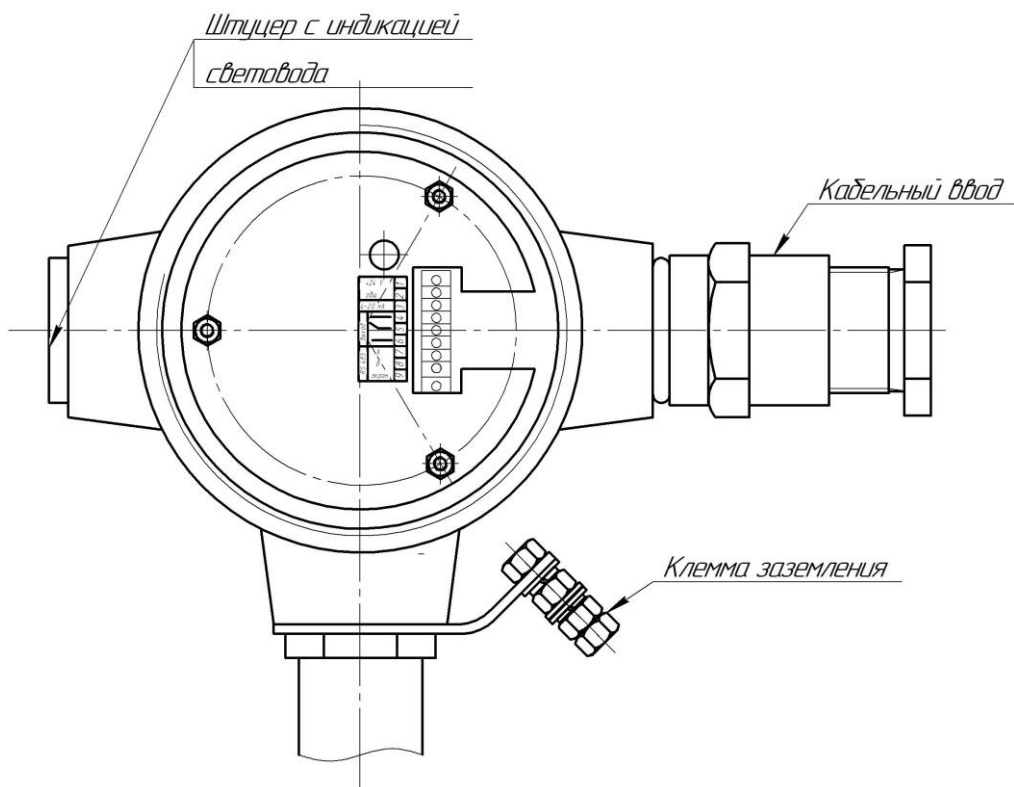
Корпус из алюминиевого сплава (IP65/IP67).
